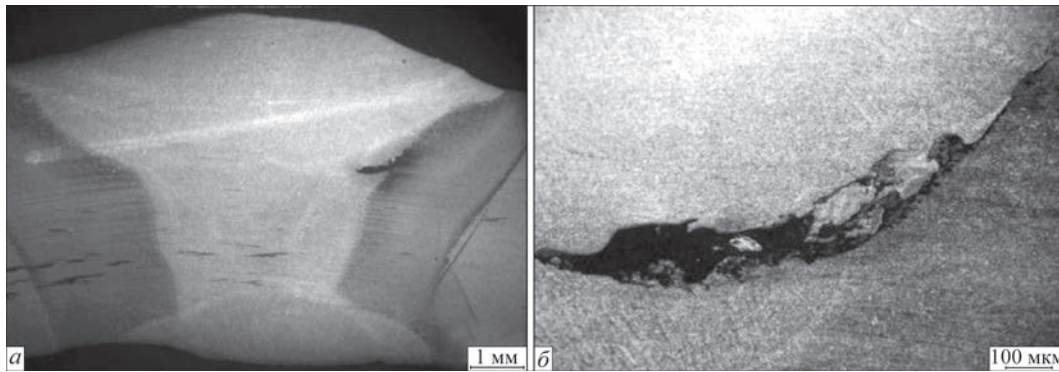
Загальний вигляд поперечного перерізу поздовжнього зварного з'єднання (а) та міжваликове несплавлення (б)
